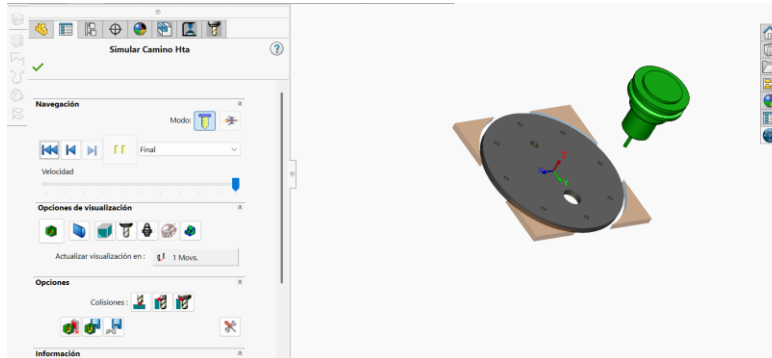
Desarrollo Cad de las partes del intercambiador de calor.
